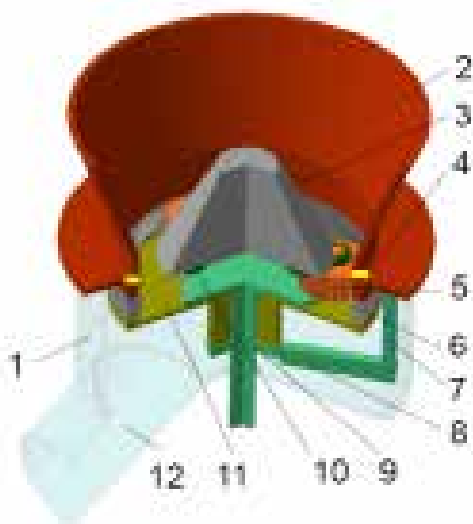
СВЧ-гранулятор с цилиндрическим резонатором: 1 — экранирующий корпус; 2 — загрузочная неферромагнитная емкость; 3 — конусообразный экран; 4 — излучатели; 5 — прижимные диэлектрические ролики; 6 — неферромагнитная цилиндрическая матрица; 7 — нож; 8 — скребок; 9 — вал электропривода; 10 — верхняя и нижняя диэлектрические плиты для крепления прижимных роликов; 11 — цилиндрический резонатор; 12 — выгрузной патрубок
